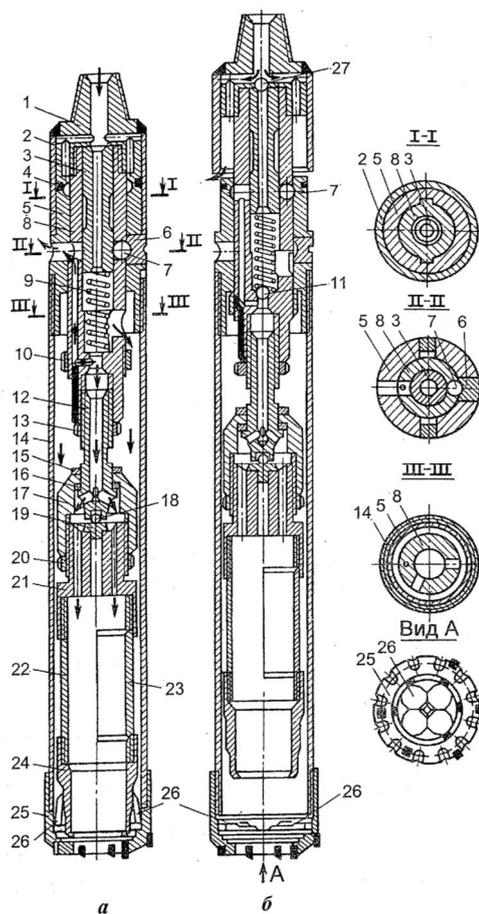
Универсальный двойной колонковый снаряд конструкции Томского политехнического институт (ДКС-У-ТПИ): 1– переходник; 2– кожух; 3– золотник; 4– сальник; 5– корпус; 6– пробка; 7– шарик-фиксатор; 8– шпindelь; 9– пружина замкового механизма; 10,13 – контргайки; 11– шаровой клапан; 12 регулировочный винт подвески; 14– наружная колонковая труба; 15– уплотнительная прокладка (сальник); 16– шайба(подшипник); 17– корпус узла подвески; 18– опорный шарик(подшипник); 19– подпятник; 20 – контргайка; 21– головка керноприёмника; 22, 23– разрезной керноприемник; 24–стакан; 25– коронка; 26– кернорвательные пластины (клапаны); 27– шаровой клапан
